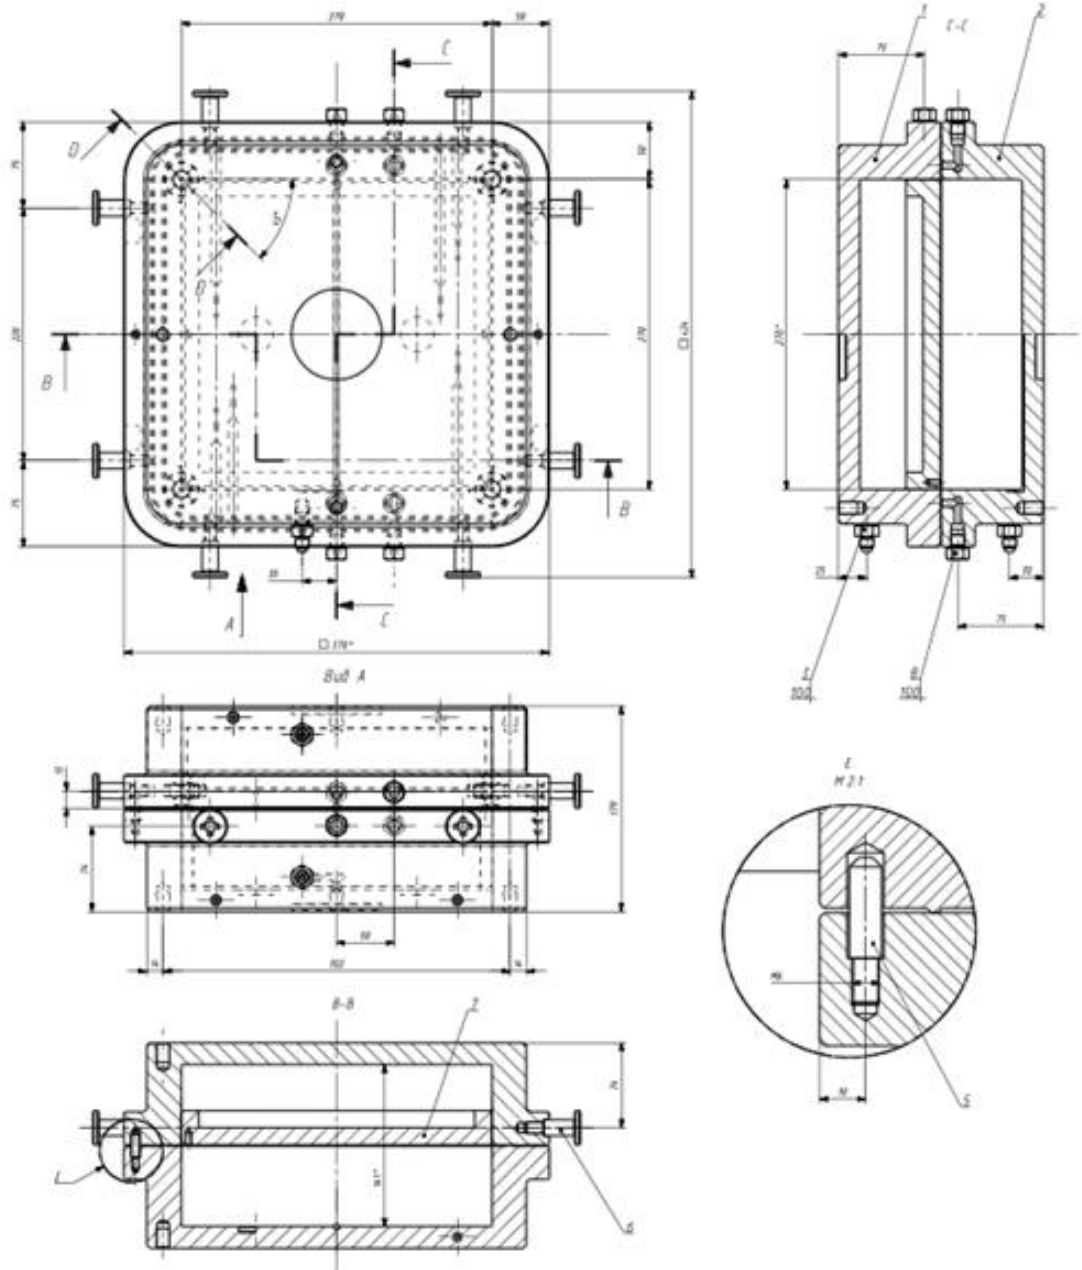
Схема блока с двумя формовочными полостями
